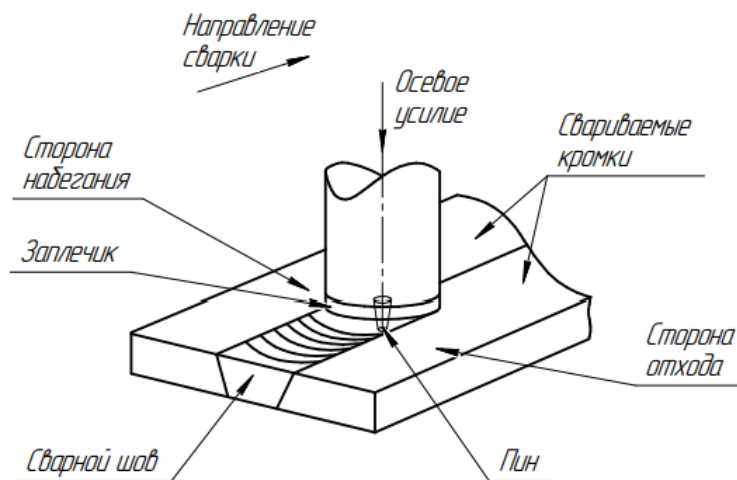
Схема рабочего процесса сварки трением с перемешиванием
